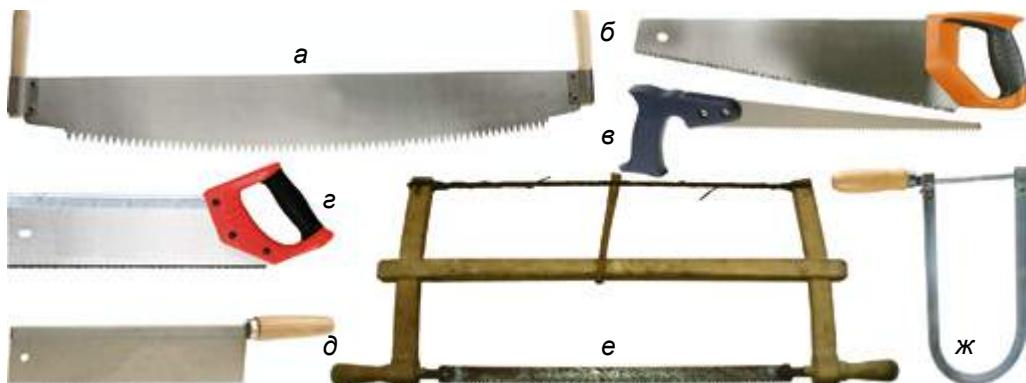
Виды столярных пил: а – поперечная двуручная; б – ножовка широкая; в – ножовка узкая; г – пила с обушком; д – наградка; е – лучковая; ж – лобзик
